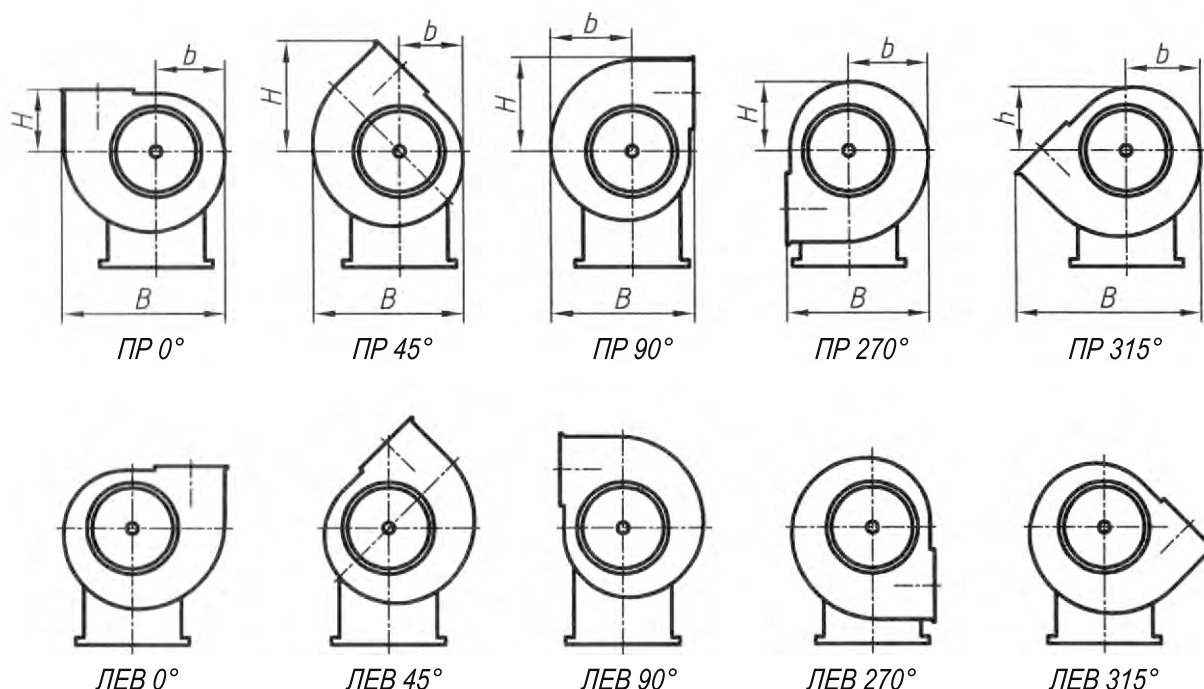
Положение корпуса вентилятора ВР 80-75 исп-1.
